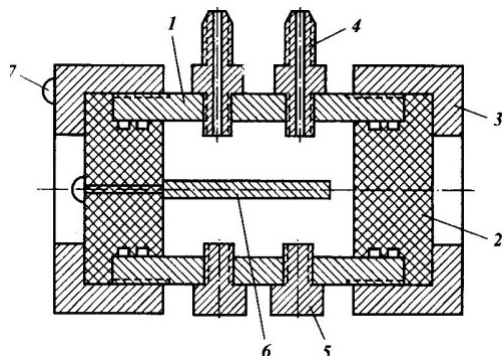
Схематическое изображение ячейки. Стальной корпус - 1; прозрачные крышки - 2; накидные гайки - 3; переходники - 4; заглушки - 5; центральный стержень, покрытый фторопластовым полым цилиндром - 6; винтовое крепление - 7
